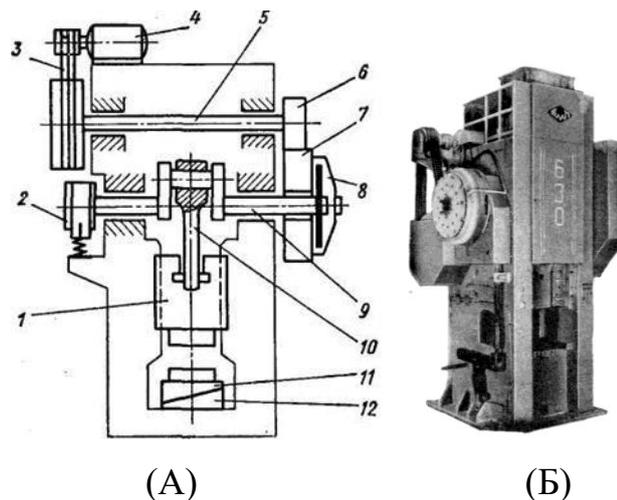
А) Кинематическая схема кривошипного горячештамповочного пресса. Б) - Горячештамповочный кривошипный пресс КА8538 усилием 630 тс
